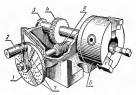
Устройство делительной головки УДГ: 1— двск; 2— рукоятка; 3— шпиндель; 4— червячное колесо; 5— червик; 6—трехнулачновый патров; 7—нож-ки скитора.
